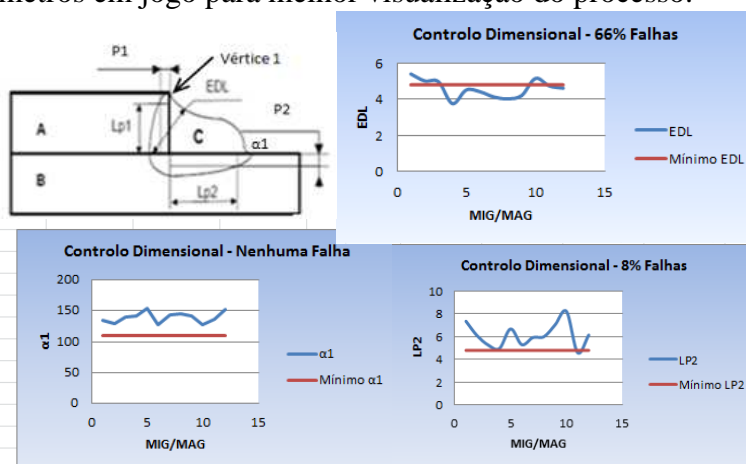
Comportamento dos parâmetros dimensionais α_1 , EDL e LP2 da soldadura MIG/MAG convencional.
